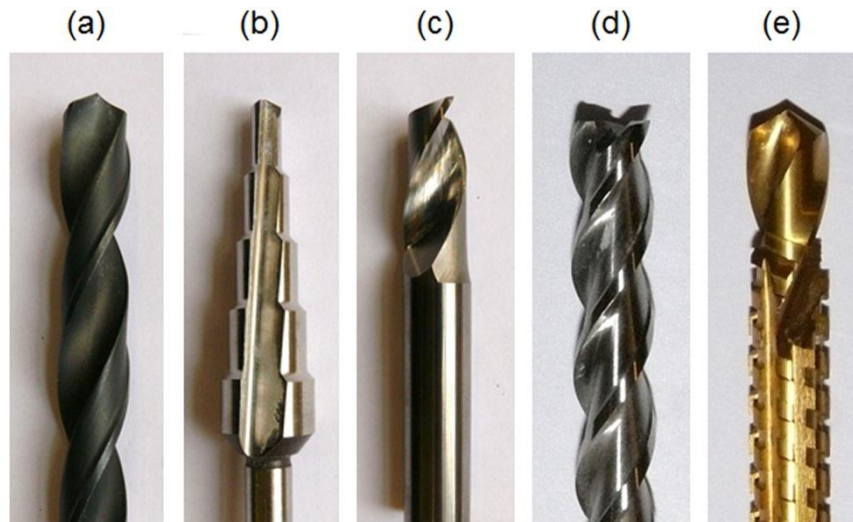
Versuchswerkzeuge: (a) Wendelbohrer, (b) Stufenbohrer, (c) Einzahnfräser, (d) Schafffräser, (e) Bohrfräser
